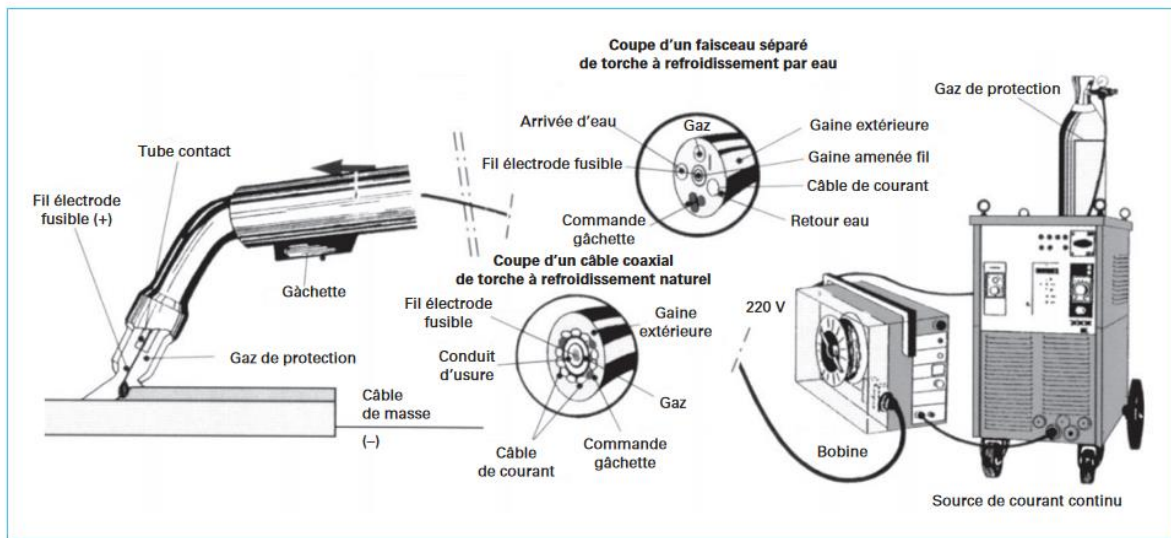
Équipement pour le soudage MIG [94].
